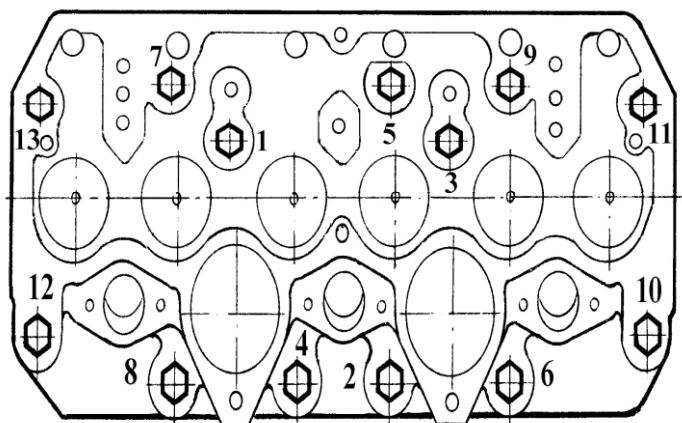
Схема последовательности затяжки болтов крепления головки цилиндров
